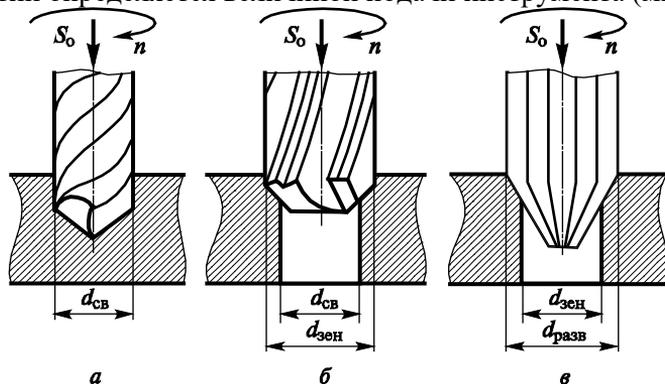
Схемы обработки деталей на сверлильном станке осевым инструментом: *a* — сверление; *б* — зенкерование; *в* — развертывание
